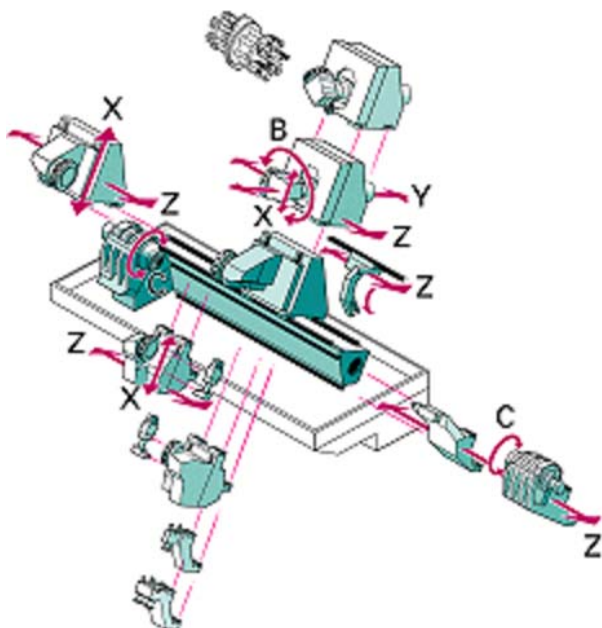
Ряд модулей токарного станка с ЧПУ Index G300
